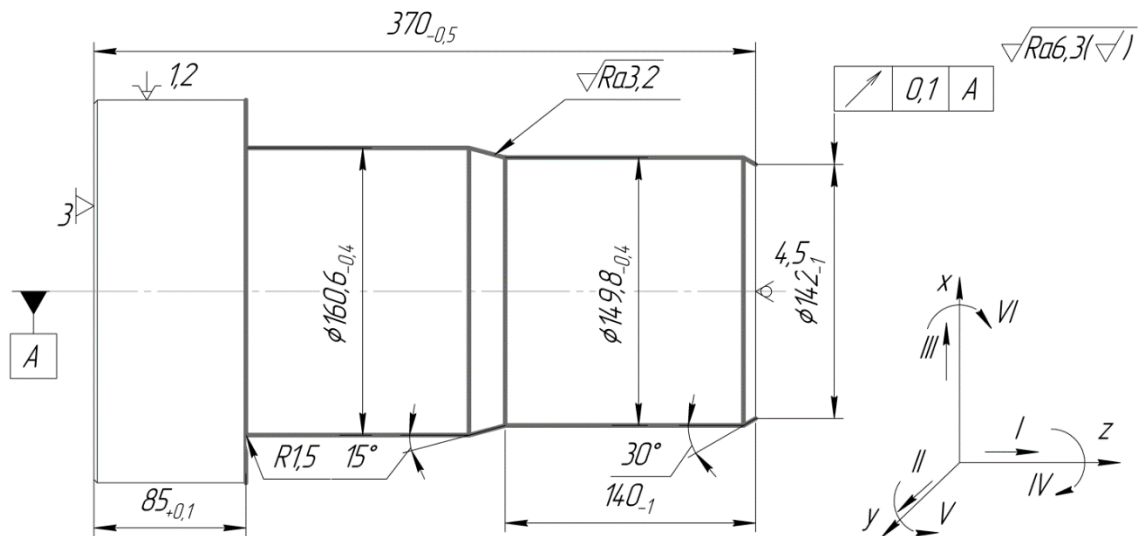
Базова схема базування на операції 050 токарної з ЧПУ
